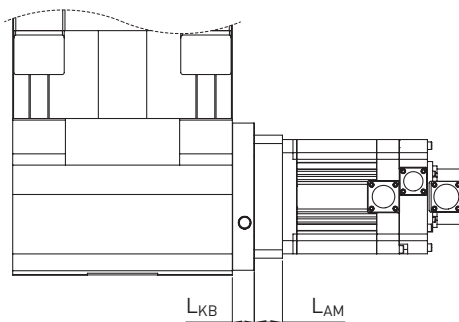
Motoranbindung Brückenachse HB-B ohne Getriebe
